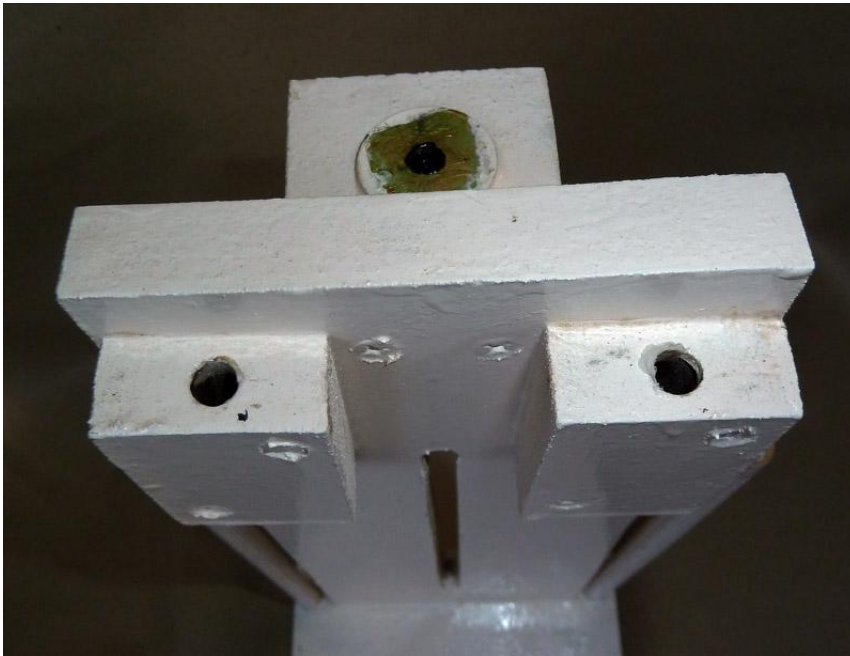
Detalle de taladros guía y apoyo metálico de la barra de control
